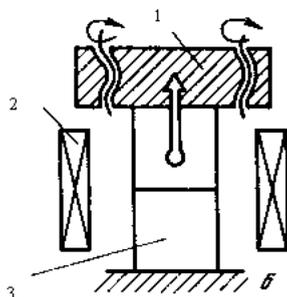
Схема диффузионной сварки принудительным деформированием:
